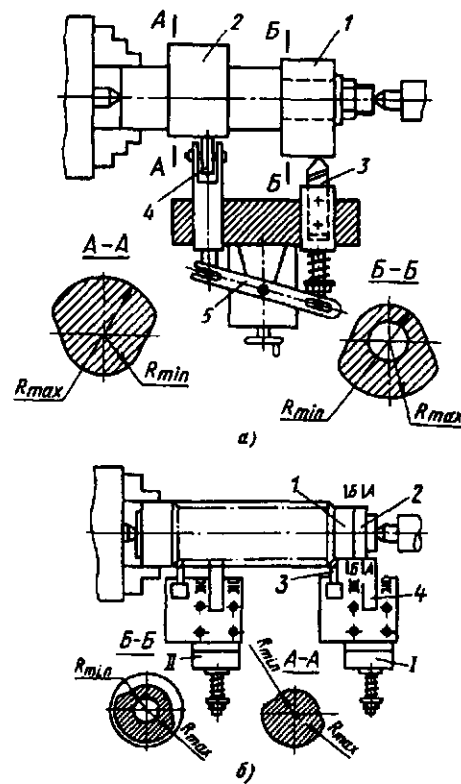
Схемы обработки кулачков по копиру: 1 – заготовка; 2 – копир; 3 – резец; 4 – шуп; 5 – рычаг. Положения: I – в начале обработки; II – в конце обработки
